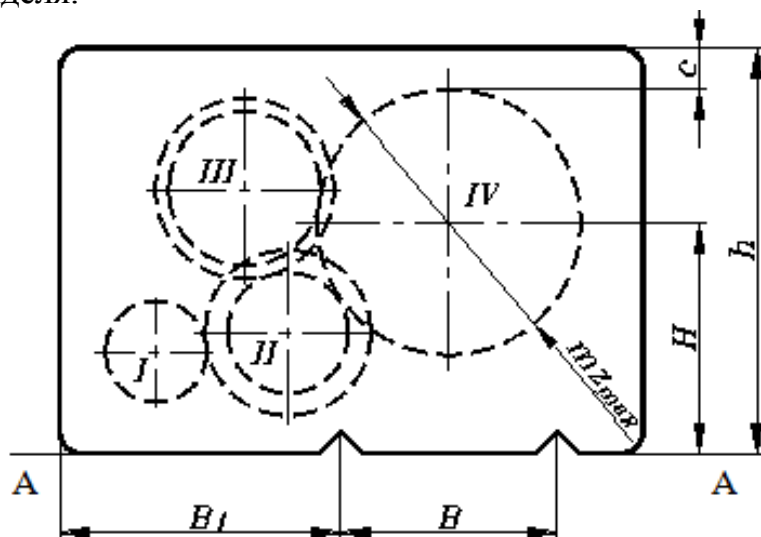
Компонировка шпиндельной бабки токарно-винторезных и токарно-револьверных станков
